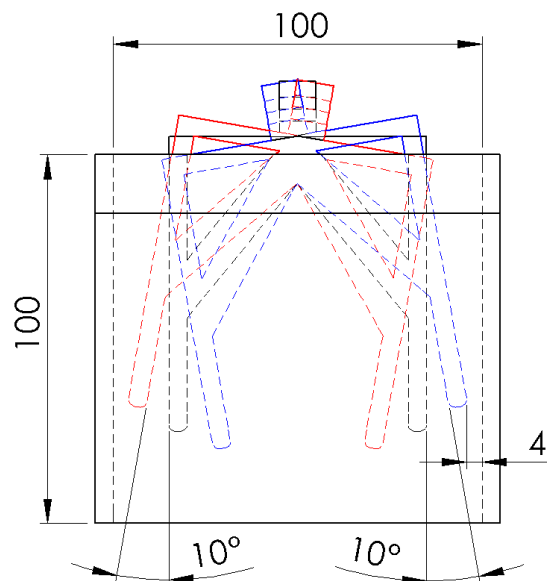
Vista planta de la interacción horquilla-tarima, unidades en mm.
